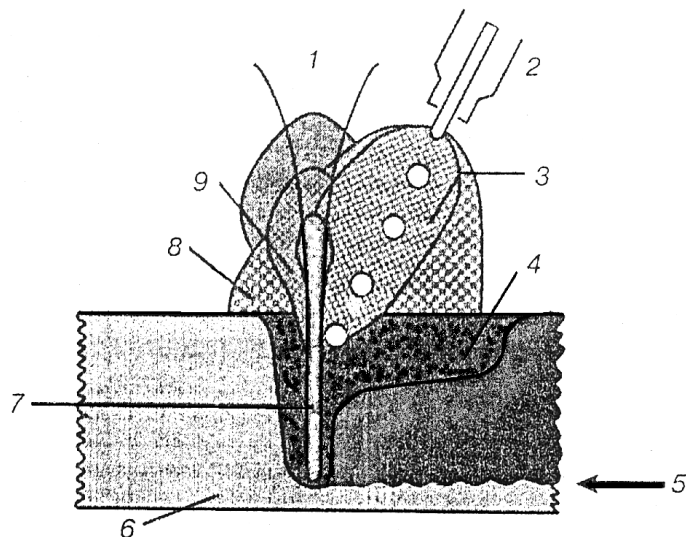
Схема процесса лазер – МИГ-сварки: 1 – лазерный луч; 2 – электрод; 3 – дуга; 4 – зона плавления; 5 – направление сварки; 6 – изделие; 7 – паровой канал; 8 – плазма; 9 – пары металла, образующиеся под действием лазерного излучения
